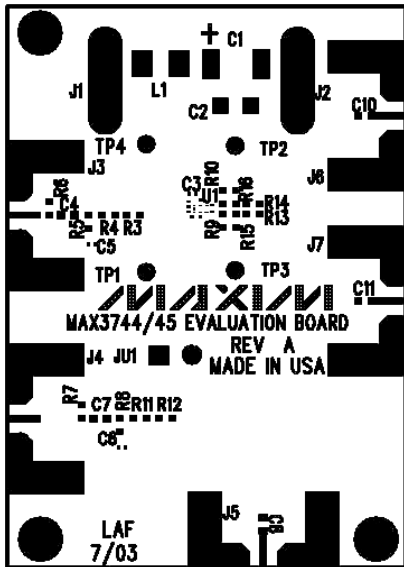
MAX3744/MAX3745 评估板 PCB 元件布局
